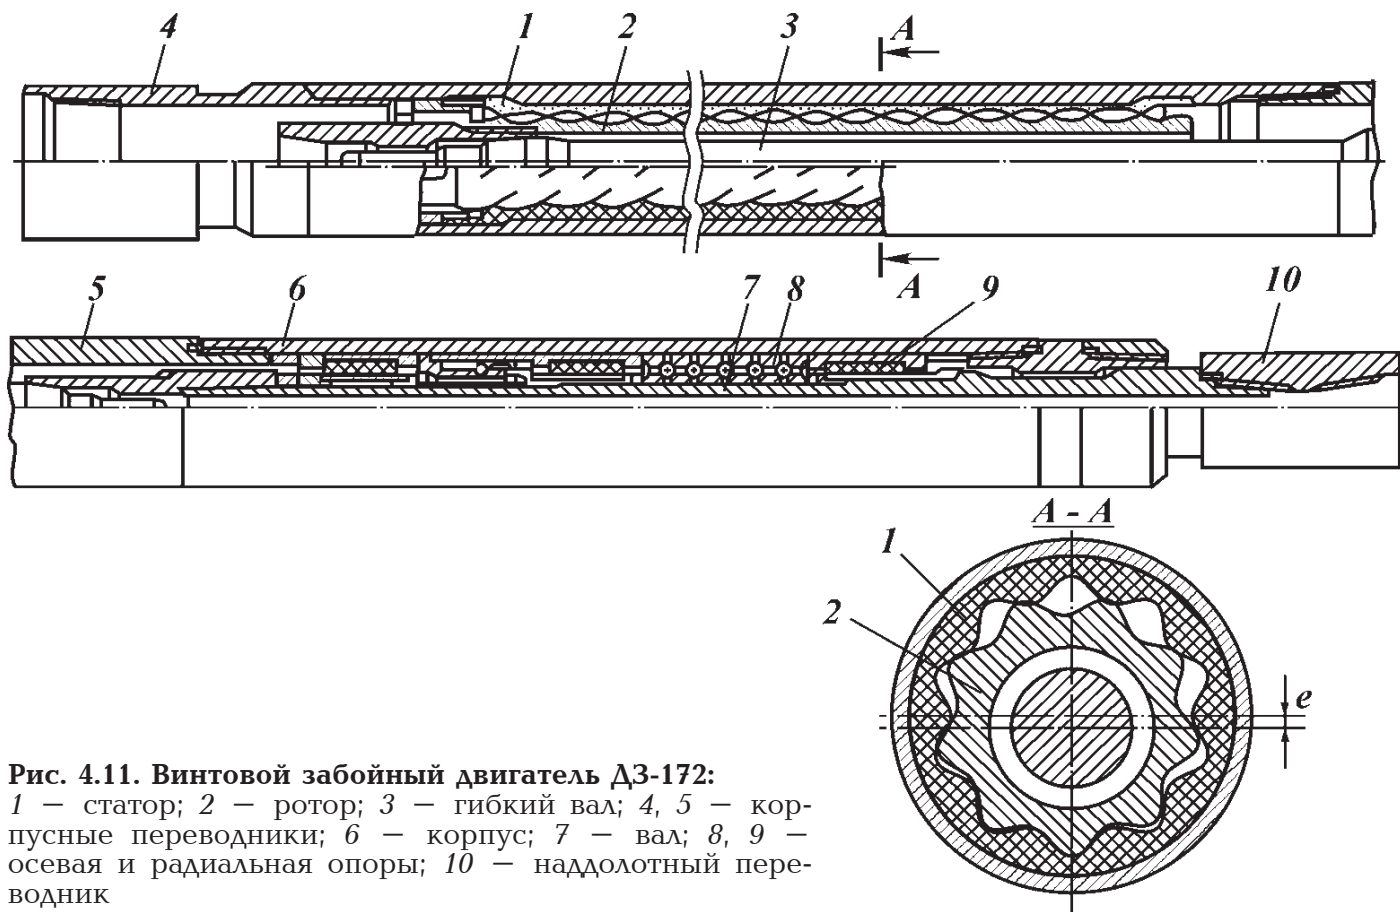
Винтовой забойный двигатель ДЗ-172:
